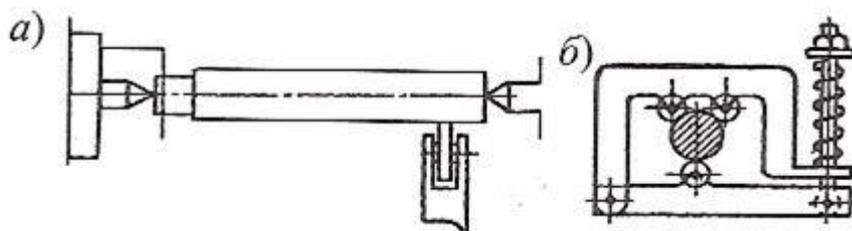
Приспособление для обкатывания цилиндрических поверхностей: а — с одним роликом; б — с тремя роликами
